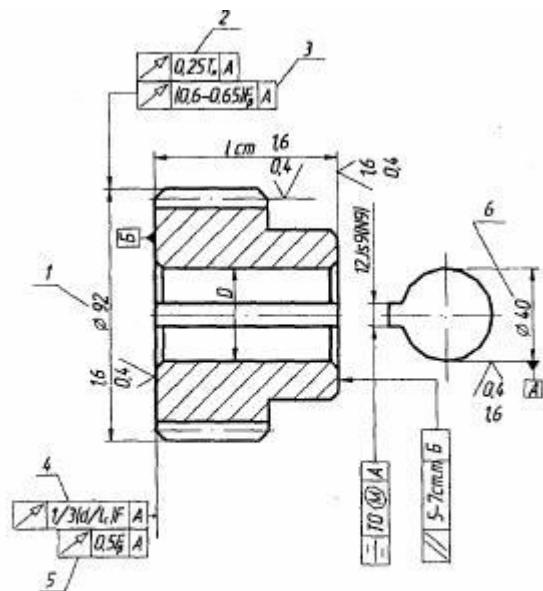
Зубчатое колесо с типовыми требованиями к точности его изготовления
